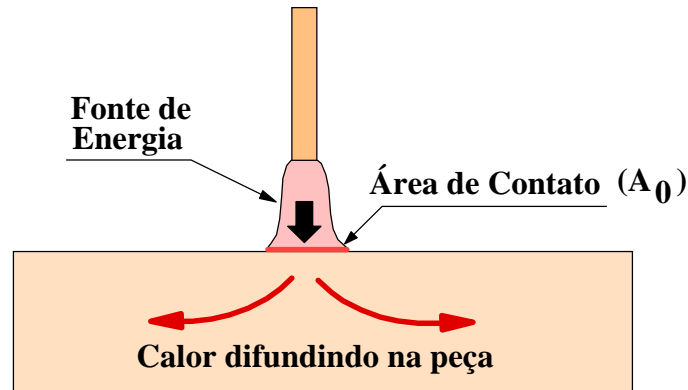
Fluxo geral de calor na soldagem por fusão.
